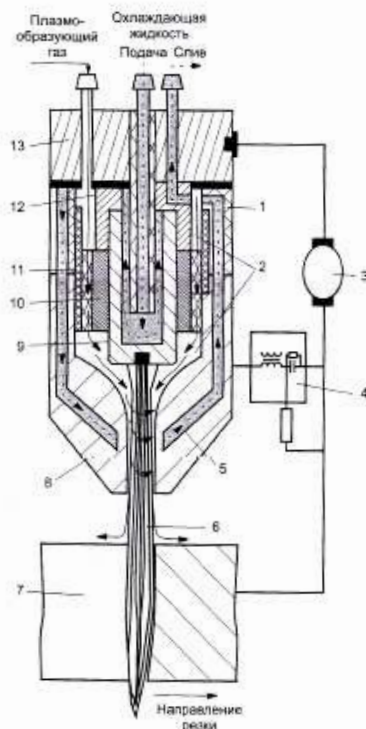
Конструктивная схема плазматрона для резки металла (прямая полярность): 1 — изолятор; 2 — ГВТ; 3 — источник питания; 4 — устройство зажигания дуги; 5 — тракт охлаждения; 6 — плазменная дуга (струя); 7 — металл (анод); 8 — сопло (анод); 9 — электрод (катод); 10 — завихритель; 11 — уплотняющая втулка; 12 — катододержатель; 13 — хвостовик
